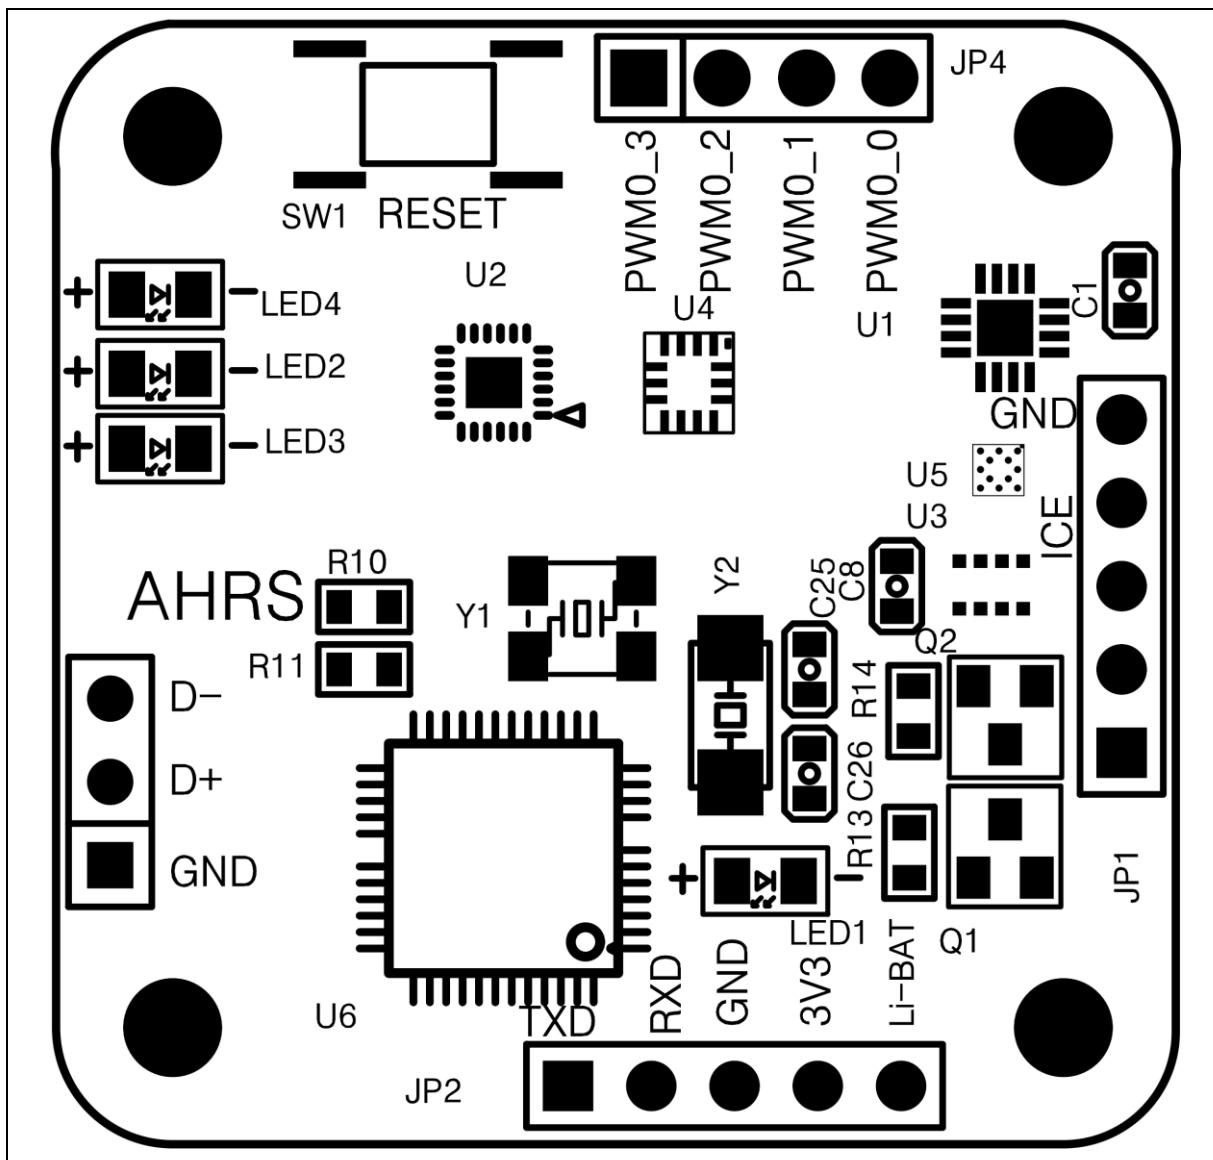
AHRS 模組主控端正面 PCB 佈局
